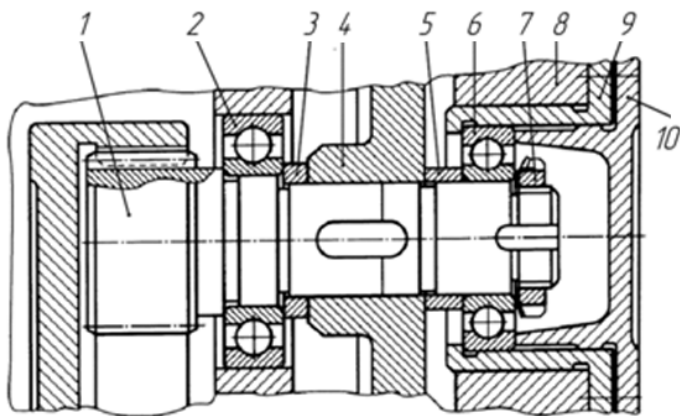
Конструкция крепления вала цилиндрического редуктора
